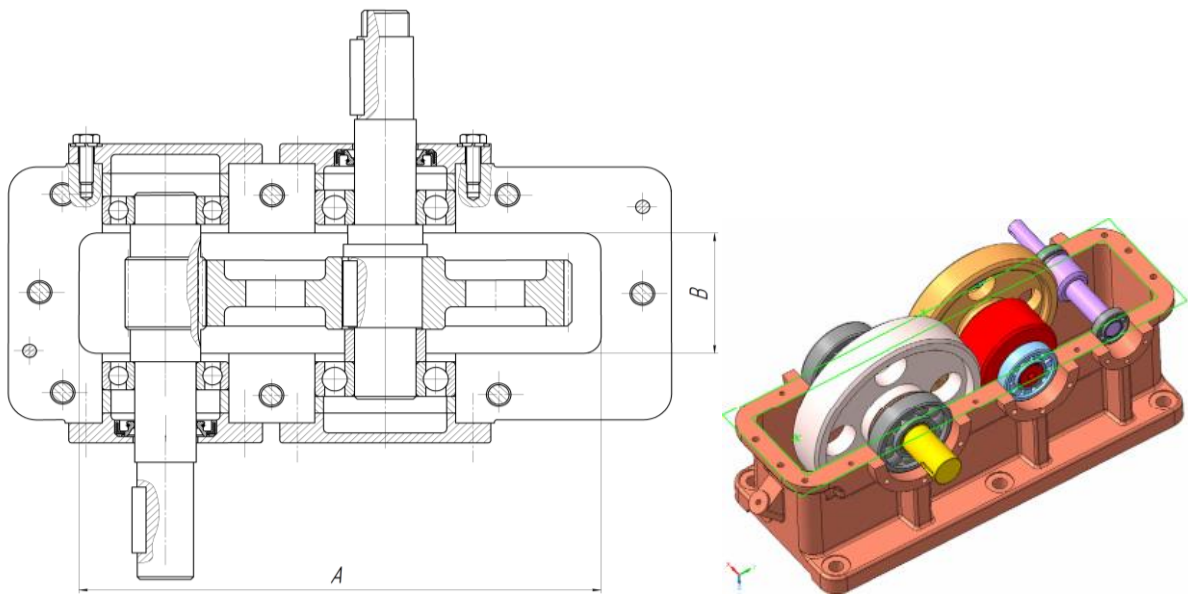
Розміри внутрішньої частини корпусу
